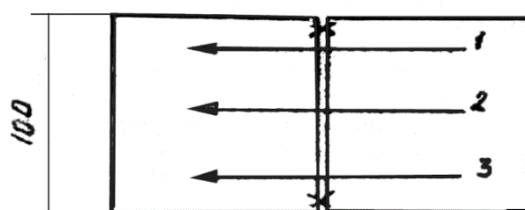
Схема наплавки валиков (x – прихватки).
